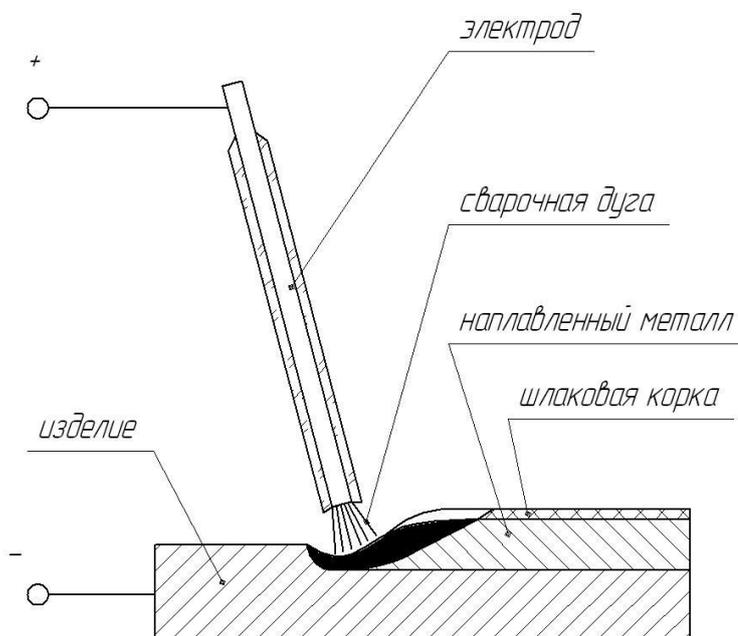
Схема выполнения ручной дуговой наплавки штучными электродами
